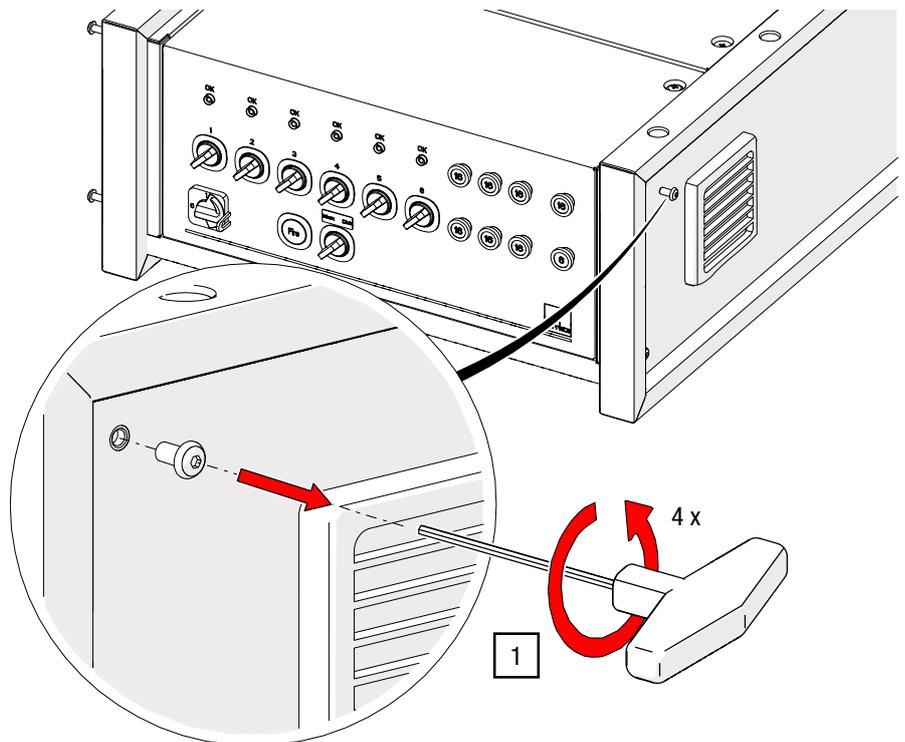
Steuerung G-FRAME Schrauben für Montagewinkel lösen
